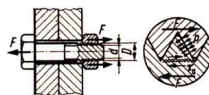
Beanspruchung einer Schraubverbindung durch Längskraft F
